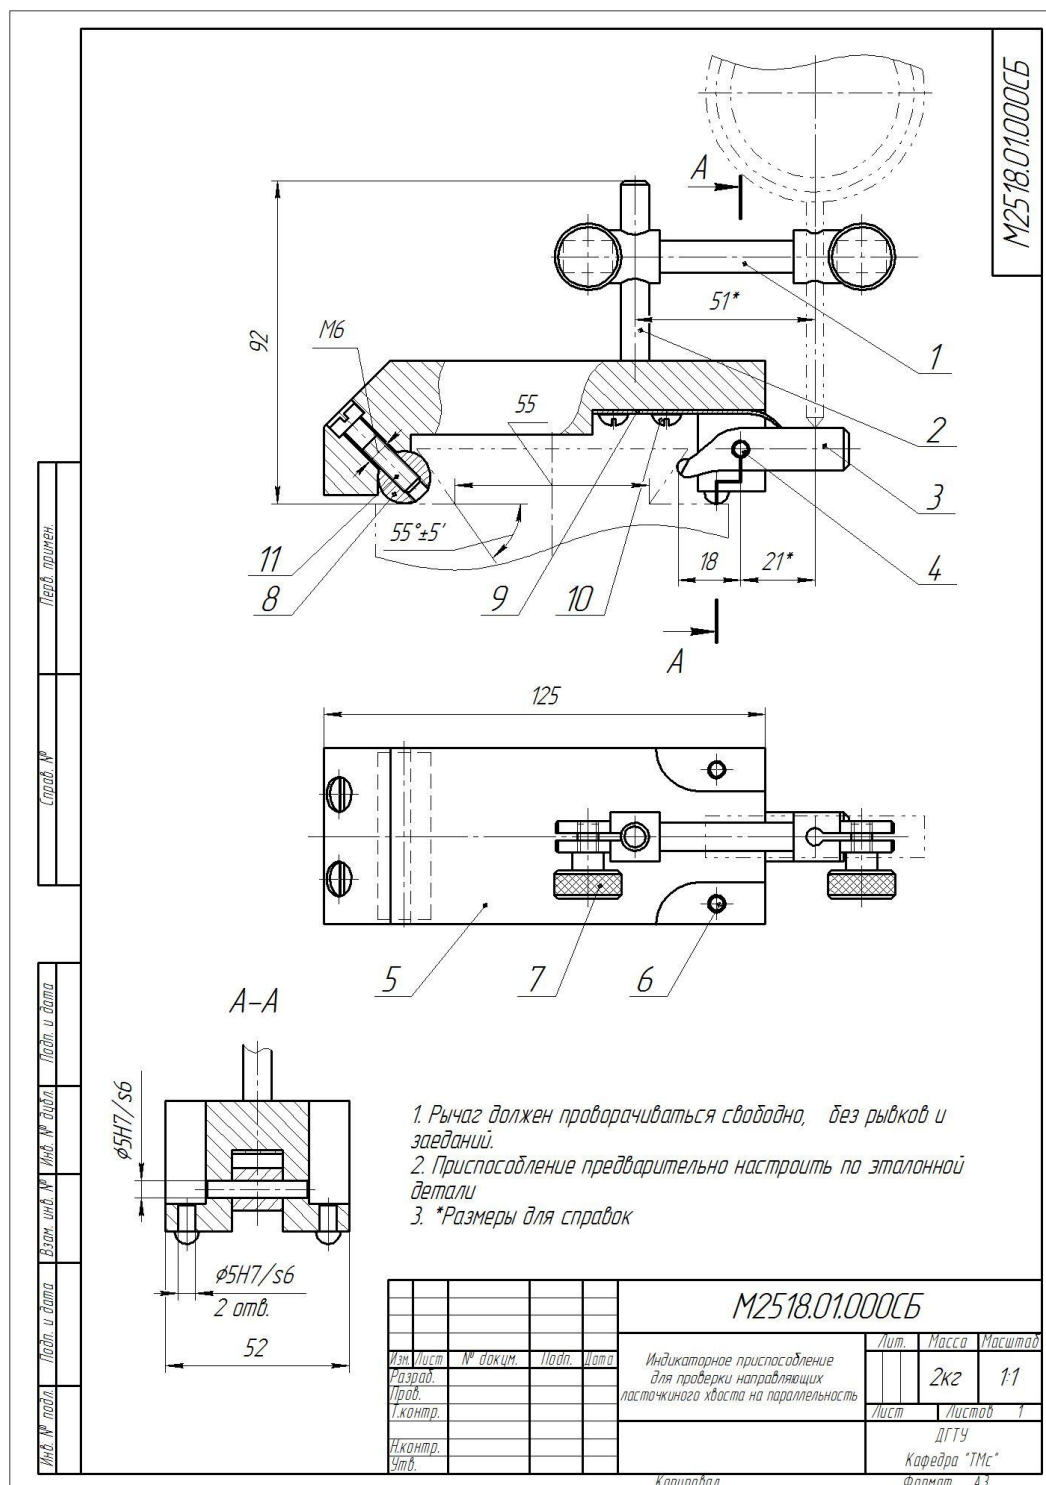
Приспособление для контроля параллельности поверхностей ласточкина хвоста
